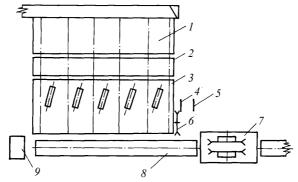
Линия обработки досок ЛОД-1П: I — поперечный конвейер; 2 — механизм поштучной выдачи; 3 — участок поперечной торцовки; 4, 5 — упоры; 6 — пила; 7 — фрезерно-обрезной станок; 8 — впередистаночный стол; 9 — пульт управления
